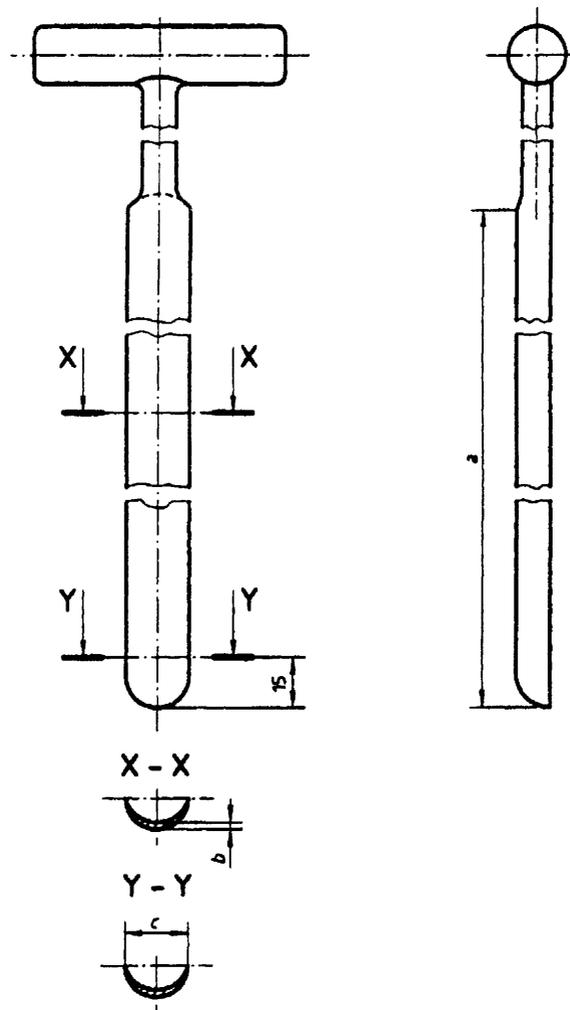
Butterbohrer (siehe Tabelle A.3)
